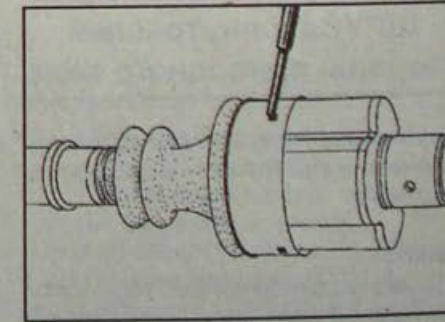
Фиксация кожуха на корпусе шарнира равных угловых скоростей
